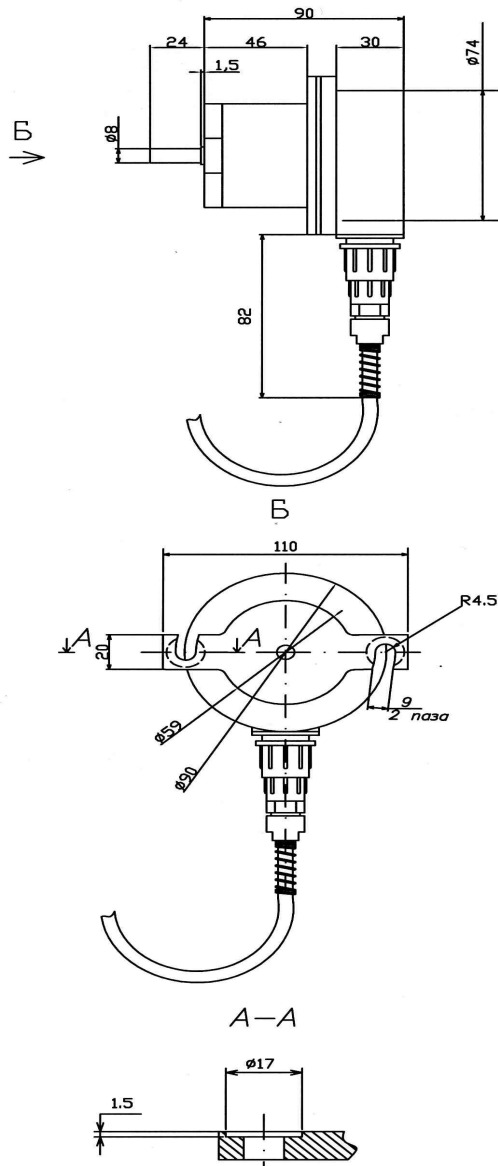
Габаритные и присоединительные размеры ДПИ .
